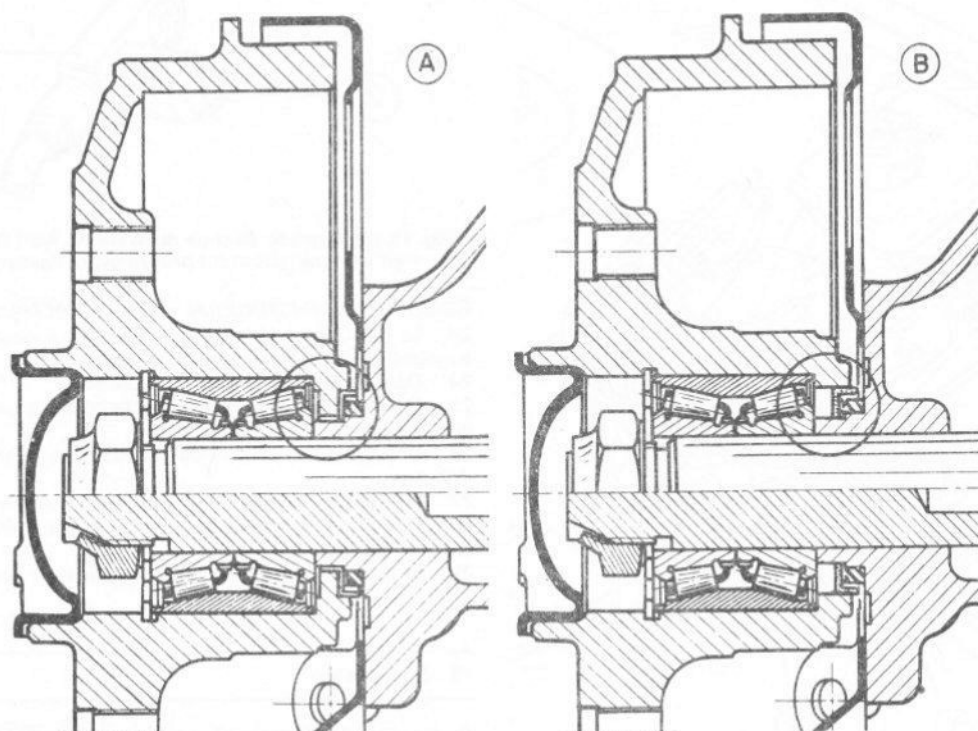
Emplacements du joint d'huile de moyeu arrière – type ancien (A) et récent (B) (Sec 19)
